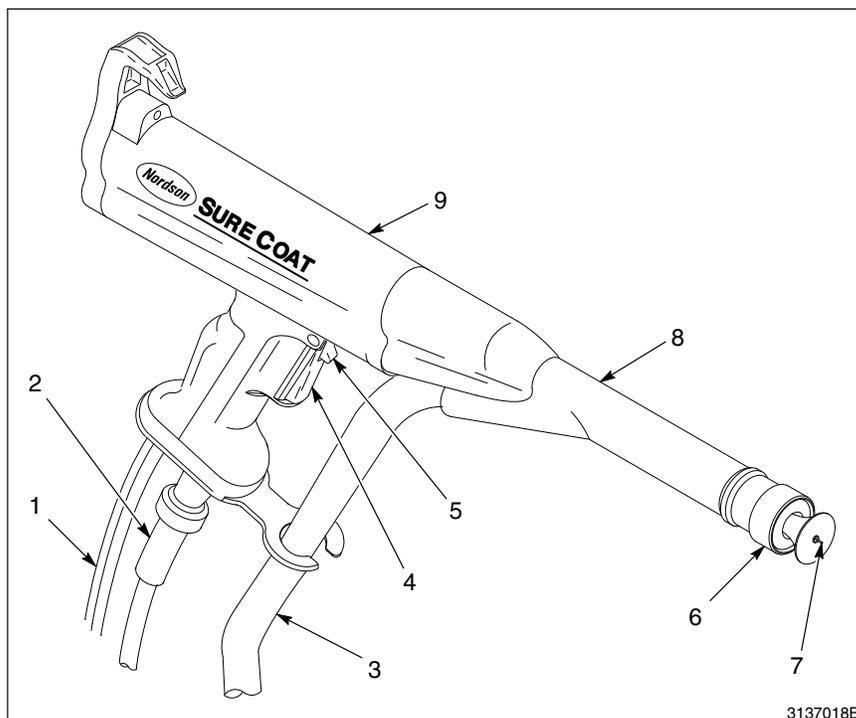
Pistolet de poudrage manuel Sure Coat
